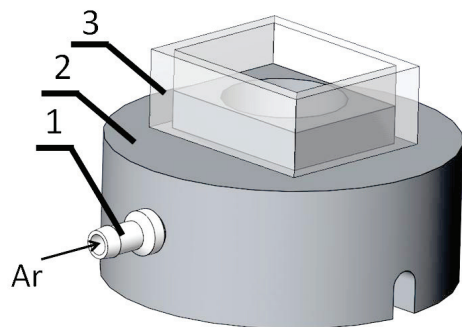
Приспособление для создания защитной среды в зоне сварки трением с перемешиванием: 1 — штуцер; 2 — держатель; 3 — камера
